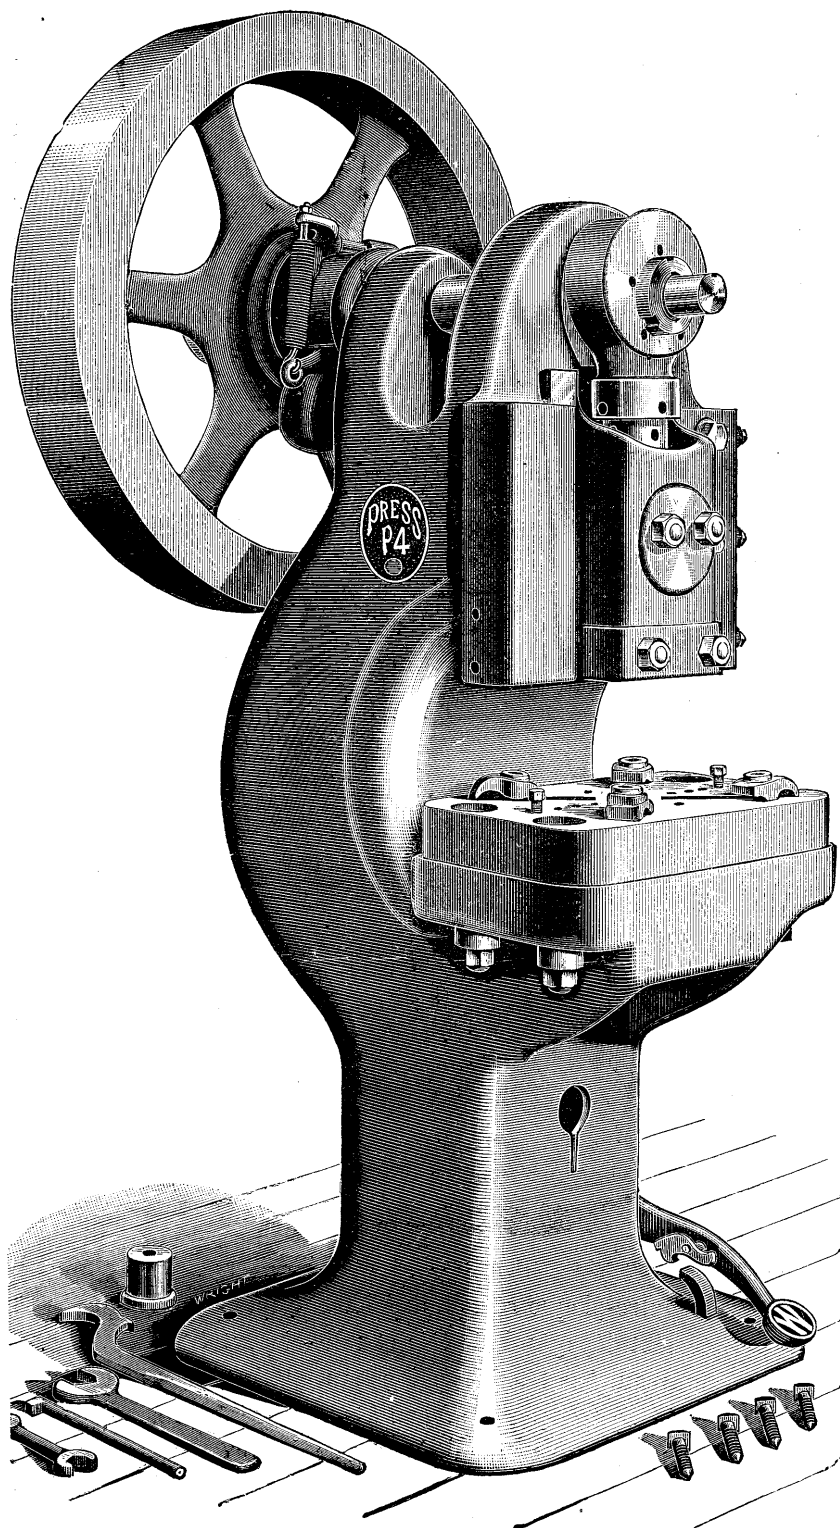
Presse à poinçonner de la Ferracute Machine Company, de Bridgeton (E.-U.).
